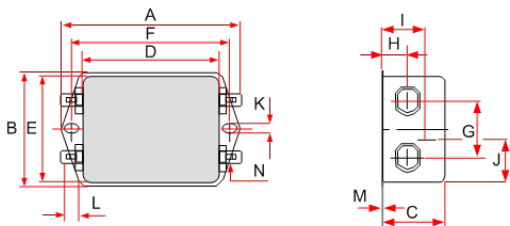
FN3258 系列 7-30A 滤波器尺寸图 (单位: mm)
